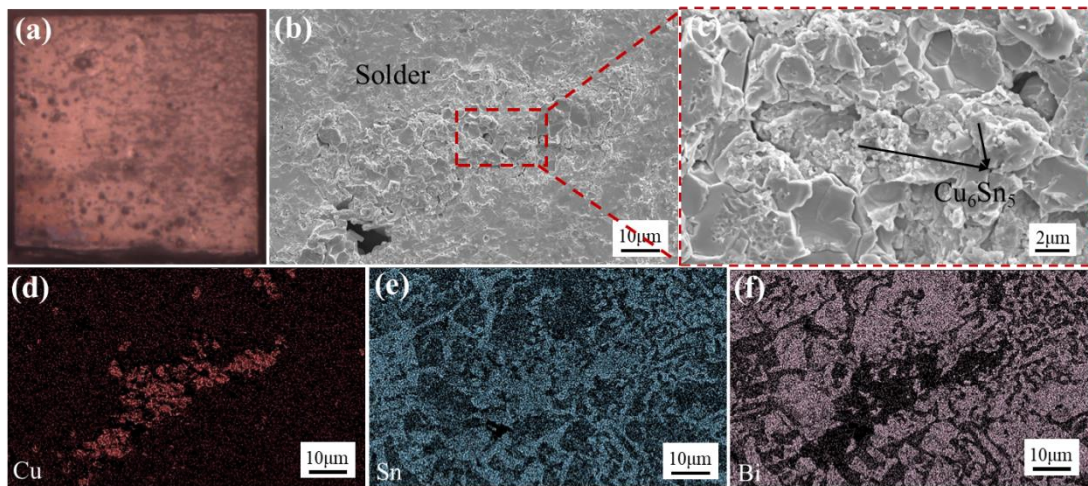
SiC-Cu 钎焊接头的断口形貌
